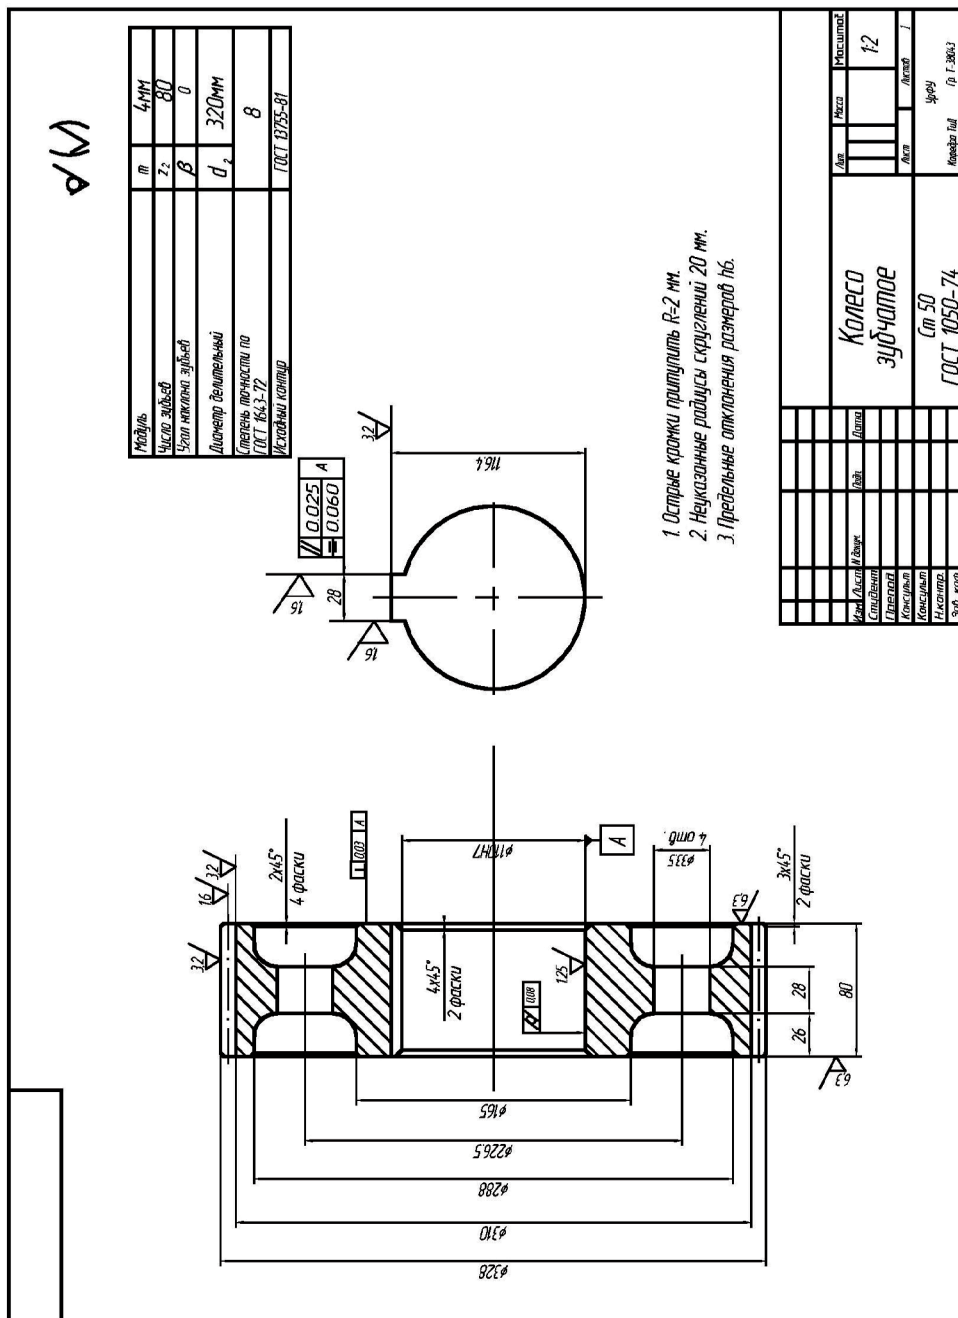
Зубчатое колесо. Рабочий чертеж
